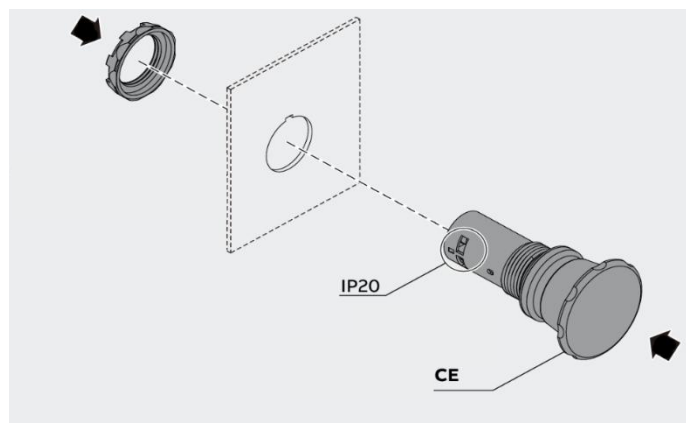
Installation du bouton coup de poing d'arrêt d'urgence
